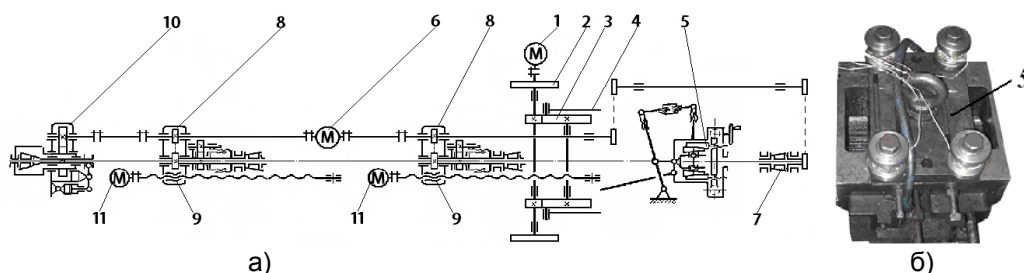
Схема комплексно модернизированного стана ХПТР 15-30 конструкции ООО «НПФ «Восток Плюс»: а – модернизированный стан с роликовой клетью; б – валковый модуль конструкции НМетАУ: 1 – электродвигатель; 2 – приводной вал с двумя маховиками; 3 – кривошипное колесо; 4 – шатуны привода клетки; 5 – рабочая клеть (роликовая или валковая с вертикальными валками); 6 – сервопривод системы группового поворота патронов; 7 – передний патрон поворота трубы; 8 – патрон поворота и подачи трубы заготовки; 9 – шарико-винтовая пара привода перемещения патронов подачи; 10 – патрон зажима стержня оправки; 11 – сервопривод патрона поворота и подачи трубы заготовки
